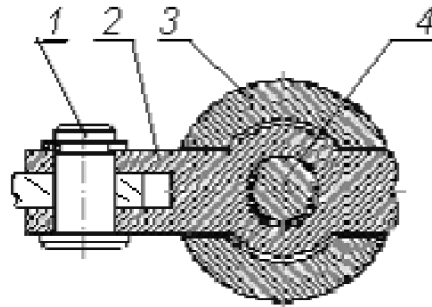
Конструкція гайки (А – А, рис.1)
